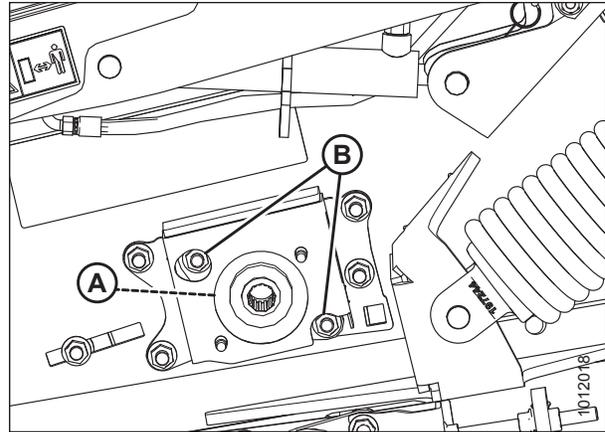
Rodillo de mando de la plataforma frontal izquierda
